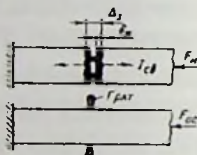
Схема образования соединения при стыковой сварке оплавлением (F_n — начальное усилие; $F_{ос}$ — усилие осадки; Δ_z — зазор между деталями; δ — слой расплавленного металла).
